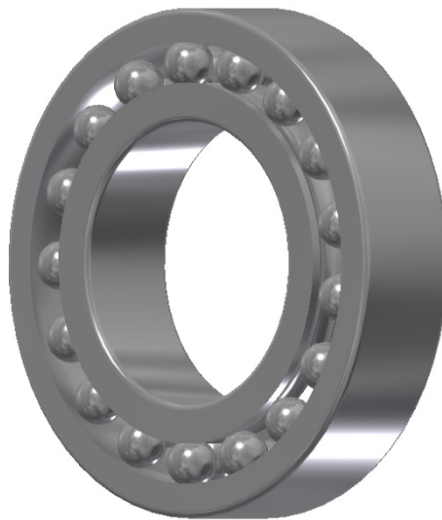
Rodamientos de bolas autoalineados, doble fila.
